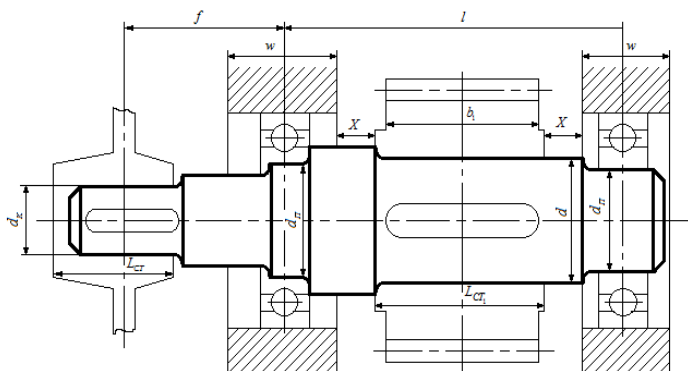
К определению расстояния между опорами вала цилиндрического одноступенчатого редуктора
